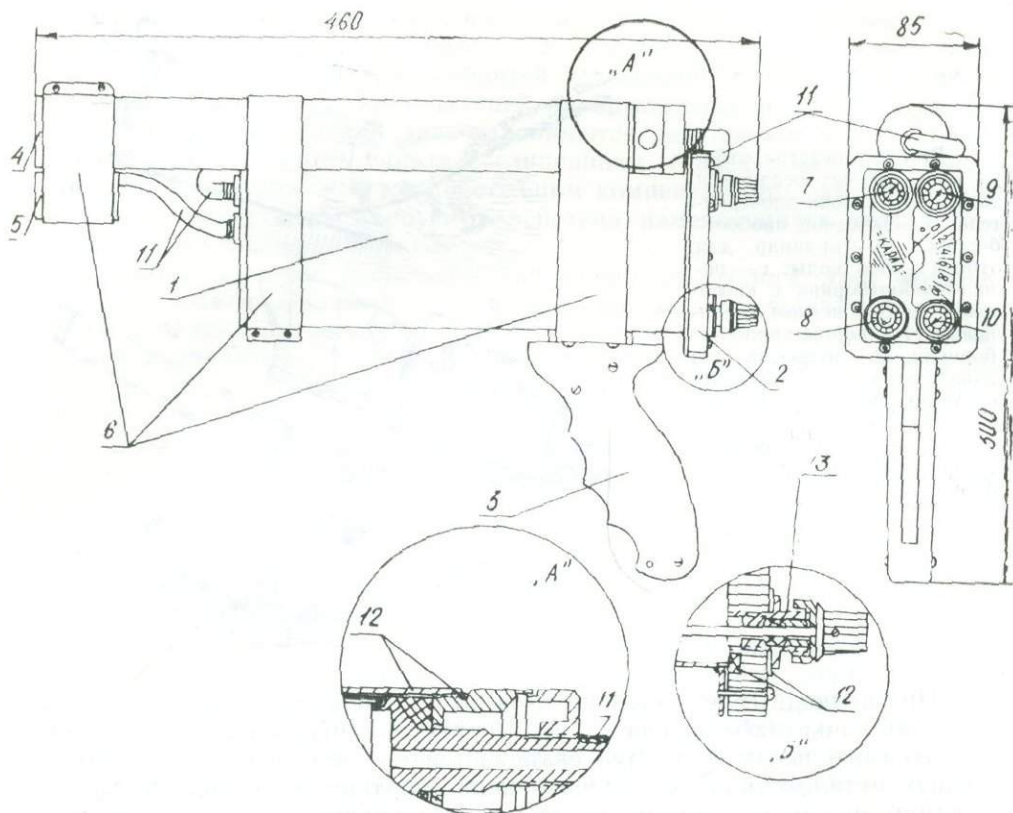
Общий вид прибора «Карад» и схема его герметизации (разработаны О. С. Корневым, В. И. Прохоровым, Я. Е. Ячником): 1 — корпус прибора из нержавеющей стали; 2 — крышка из оргстекла; 3 — рукоятка пластмассовая; 4 — датчик СРП-2 стандартный в алюминиевой гильзе, 5 — датчик типа ИМВ-2, залитый эпоксидной смолой; 6 — бандаж дюралевый; 7 — ручка диапазонов измерения капнометра; 8 — ручка установки «О» капнометра; 9 — ручка диапазонов измерений радиометра; 10 — ручка включения прибора; 11 — резиновый шланг для герметизации электровыводов; 12 — прокладки резиновые; 13 — салыник второпластовый
